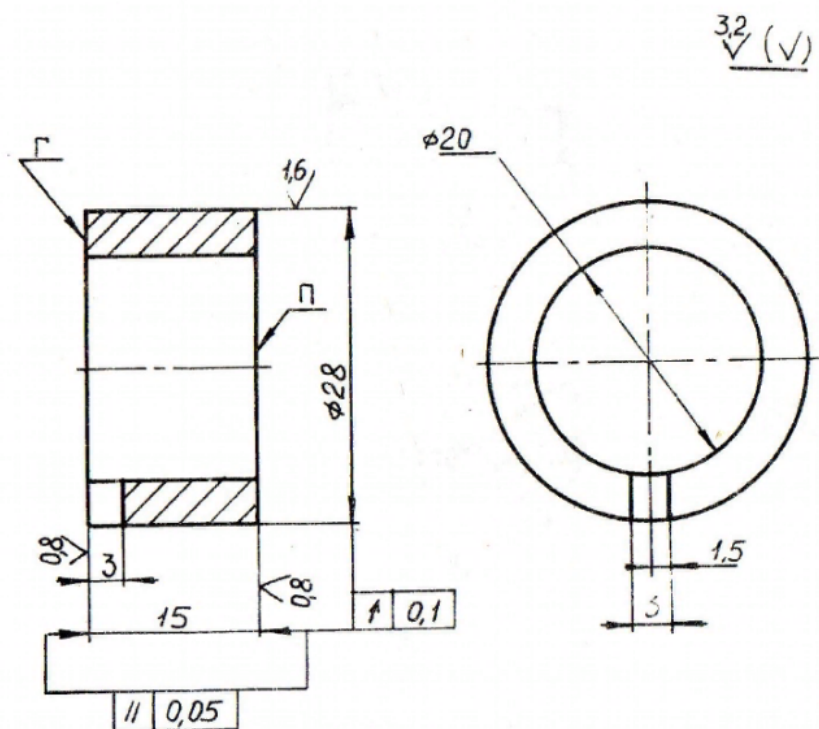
Образец – кольцо (вращающийся): П – поверхность трения, Г – поверхность клеймения
